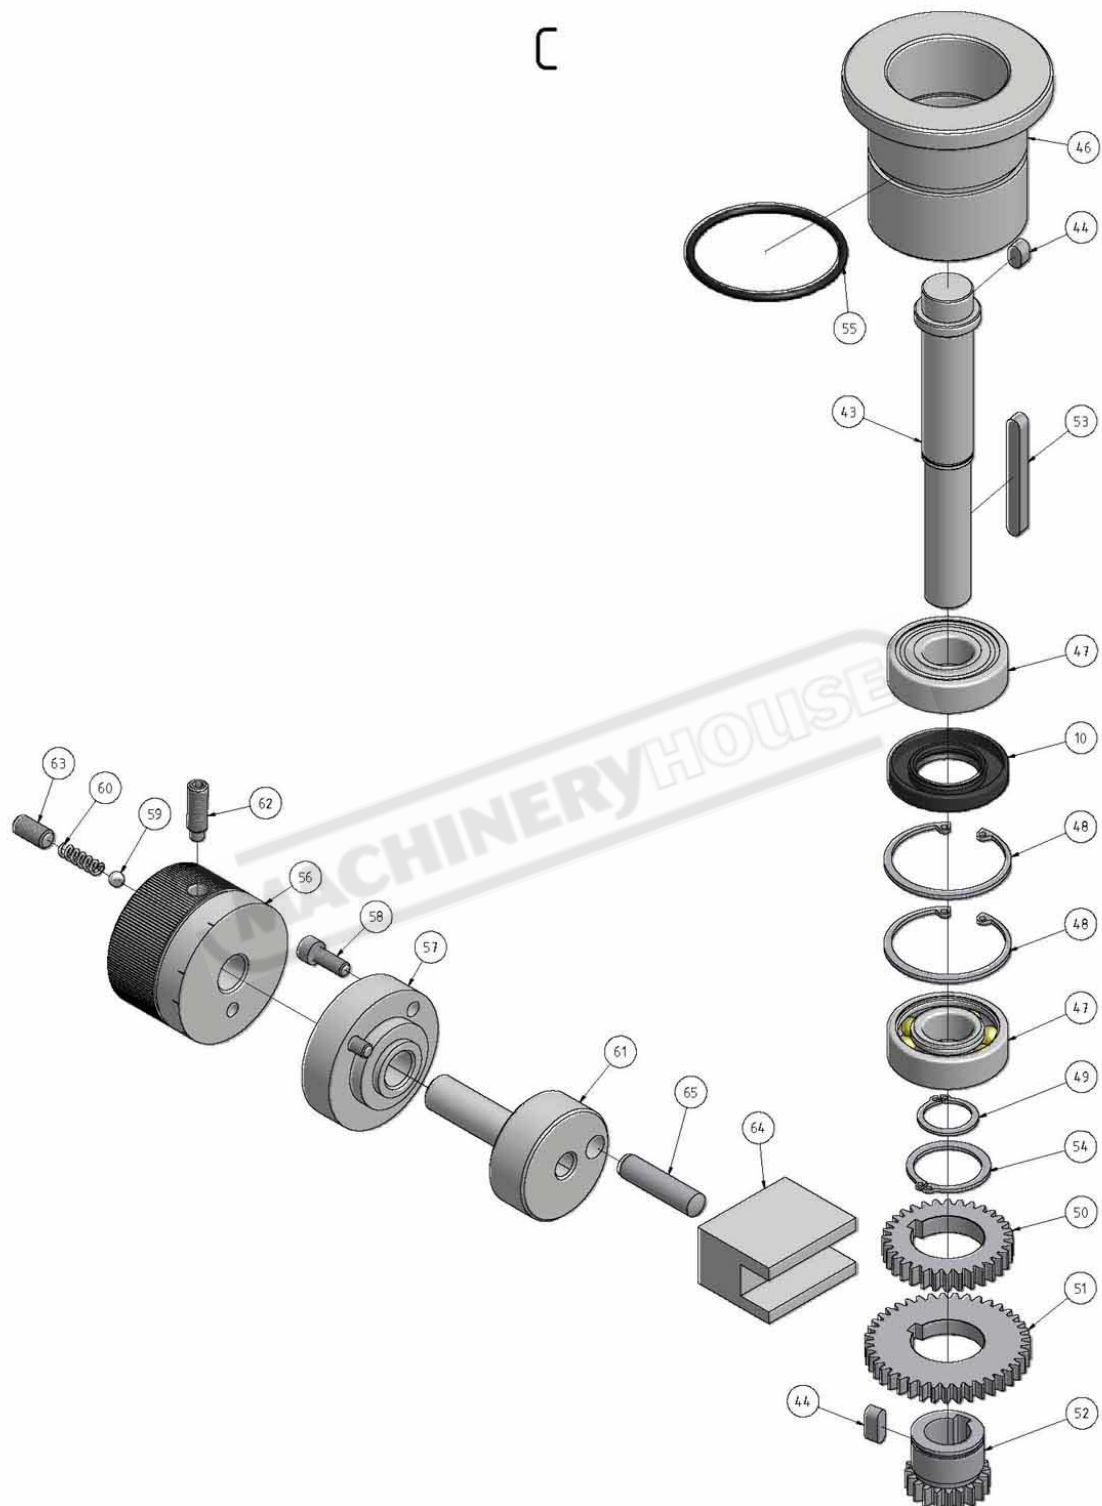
Bohrkopf 3 von 9 - Drilling head 3 of 9
